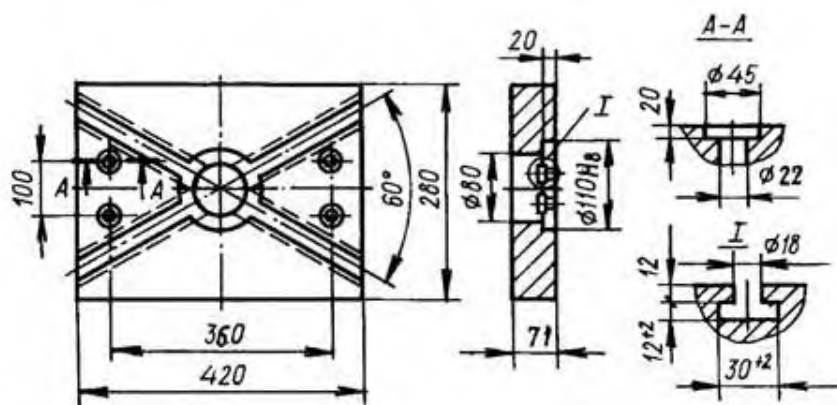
Габаритные размеры рабочего пространства пресса КД2122
